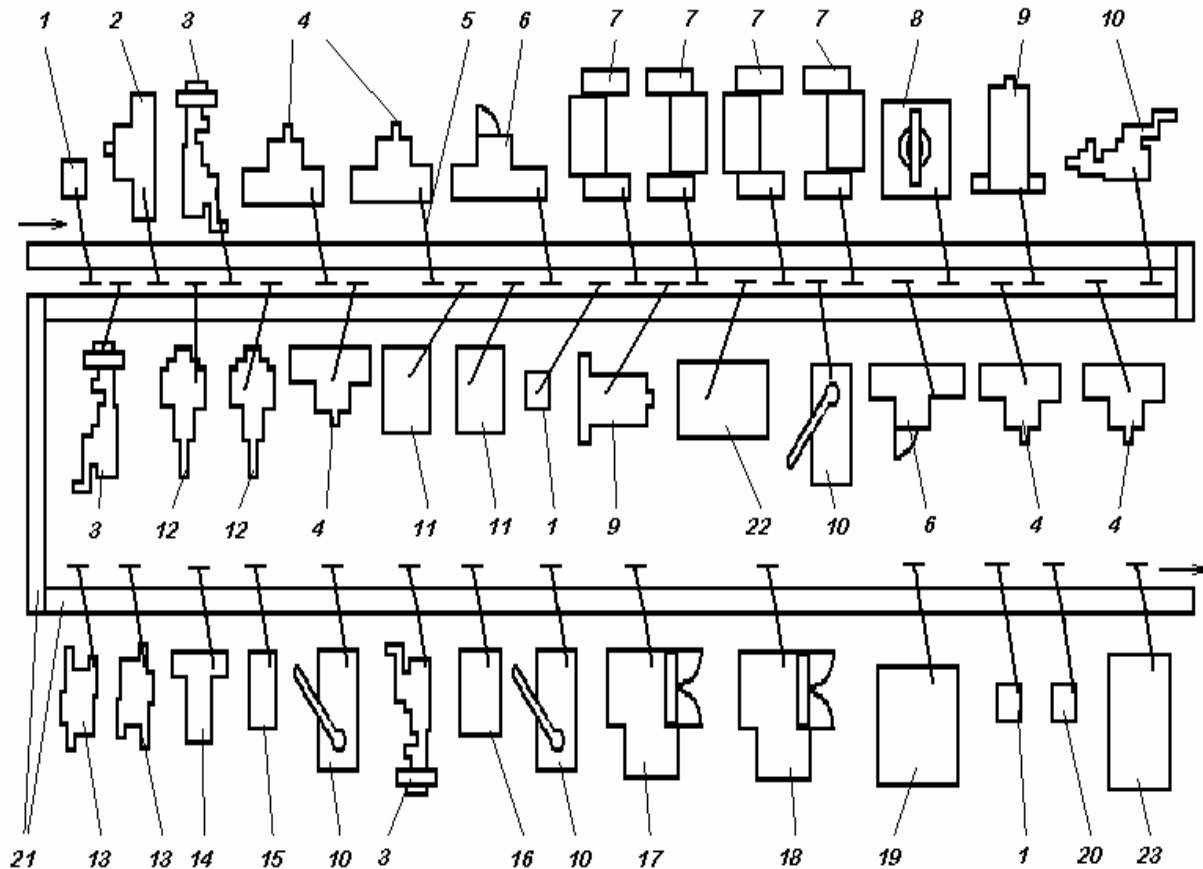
Планировка поточно-механизированной линии восстановления коленчатых валов двигателей КамАЗ-53212: 1 – магнитный дефектоскоп МД-50П; 2 – пресс гидравлический П-6326; 3 – станок токарно-винторезный 16К20; 4 – станок круглошлифовальный 3М152; 5 – подъемник пневматический 12402; 6 – станок круглошлифовальный 3В423; 7 – станок наплавочный У-653М; 8 – печь электрическая шахтная СНОЛ 1,8.1,6.3,0/1000; 9 – пресс гидравлический П-6330; 10 – станок радиально-сверлильный 2М53; 11 – полуавтомат торцешлифовальный ЗТ161Е; 12 – станок горизонтально-фрезерный 6Р83Г; 13 – полуавтомат круглошлифовальный ХШ2-12Н; 14 – полуавтомат круглошлифовальный ХШ2-01; 15 – стенд сборочный 70-7362-1518; 16 – станок балансировочный КИ-4274; 17 – полуавтомат суперфинишный 3875К; 18 – полуавтомат полировальный 3835К; 19 – установка для очистки ОМ-3600; 20 – верстак слесарный ОРГ 5365; 21 – конвейер роликовый 12398; 22 – высокочастотный генератор ВЧГ-100/0,66УЧ; 23 – ванна консервации 04.04.084.00.000
